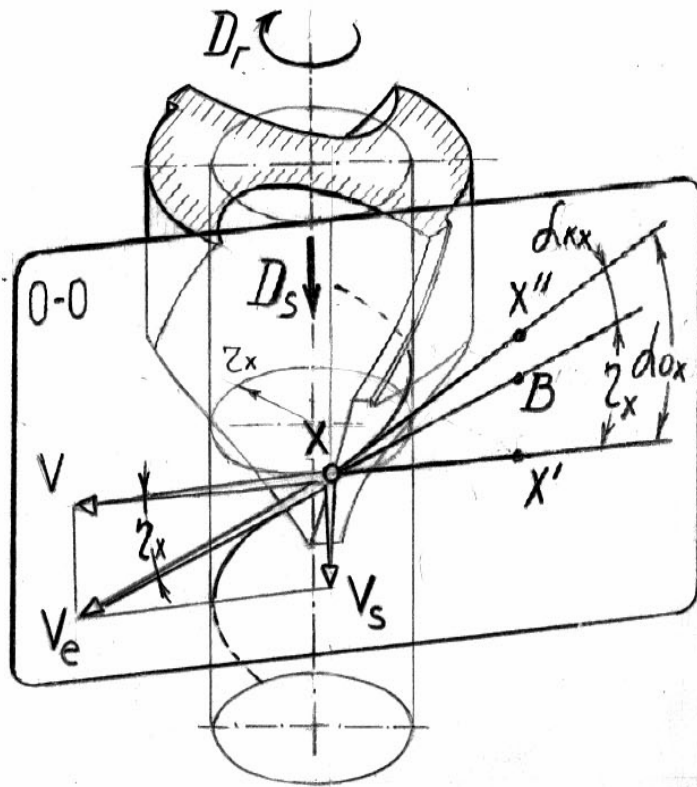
Схема к определению кинематического заднего угла при сверлении
